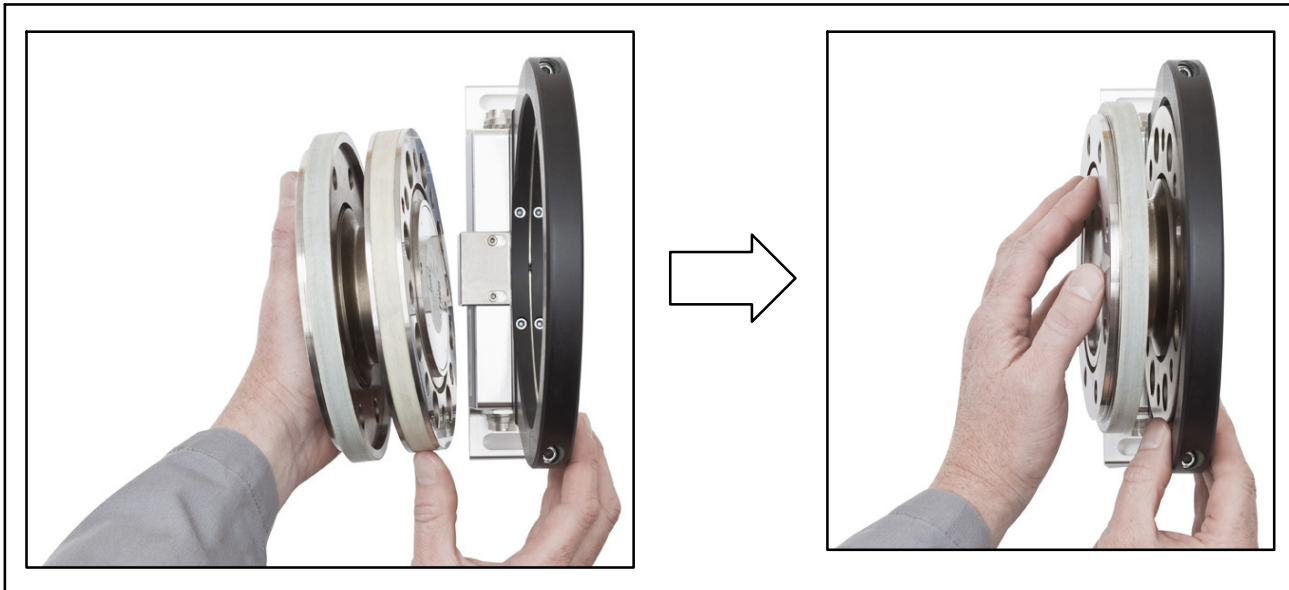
Ausrichten des Rotors mit dem Stator
